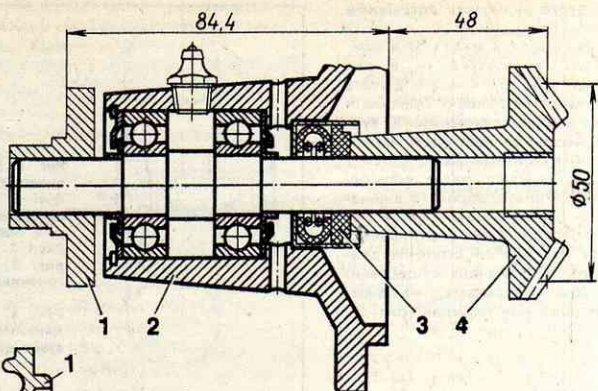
Крышка водяного насоса конструкции Е. Терлецкого: 1 — ступица шлица; 2 — крышка в сборе с подшипниками; 3 — сальник; 4 — крыльчатка.
